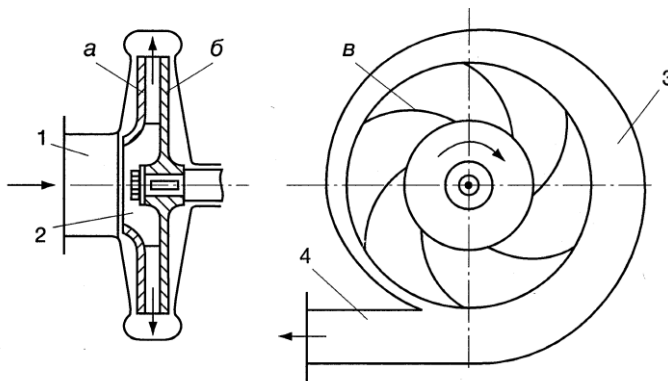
Схема відцентрового вентилятора: 1 – всмоктуючий патрубок; 2 – робоче колесо; 3 – корпус; 4 – дифузор; *а* – покривний та *б* – основний диски; *в* – лопаті
